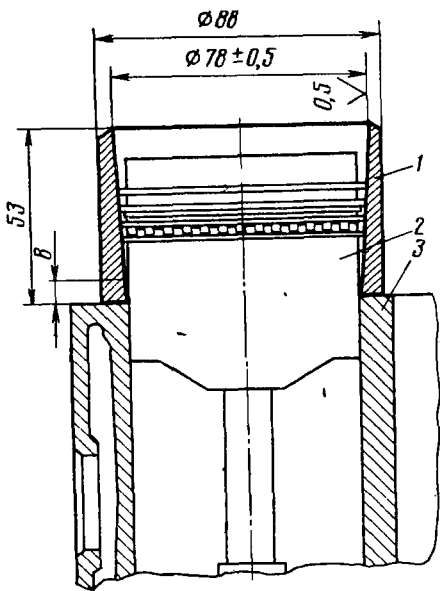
Оправка для установки поршня с кольцами и шатуном в цилиндр:
